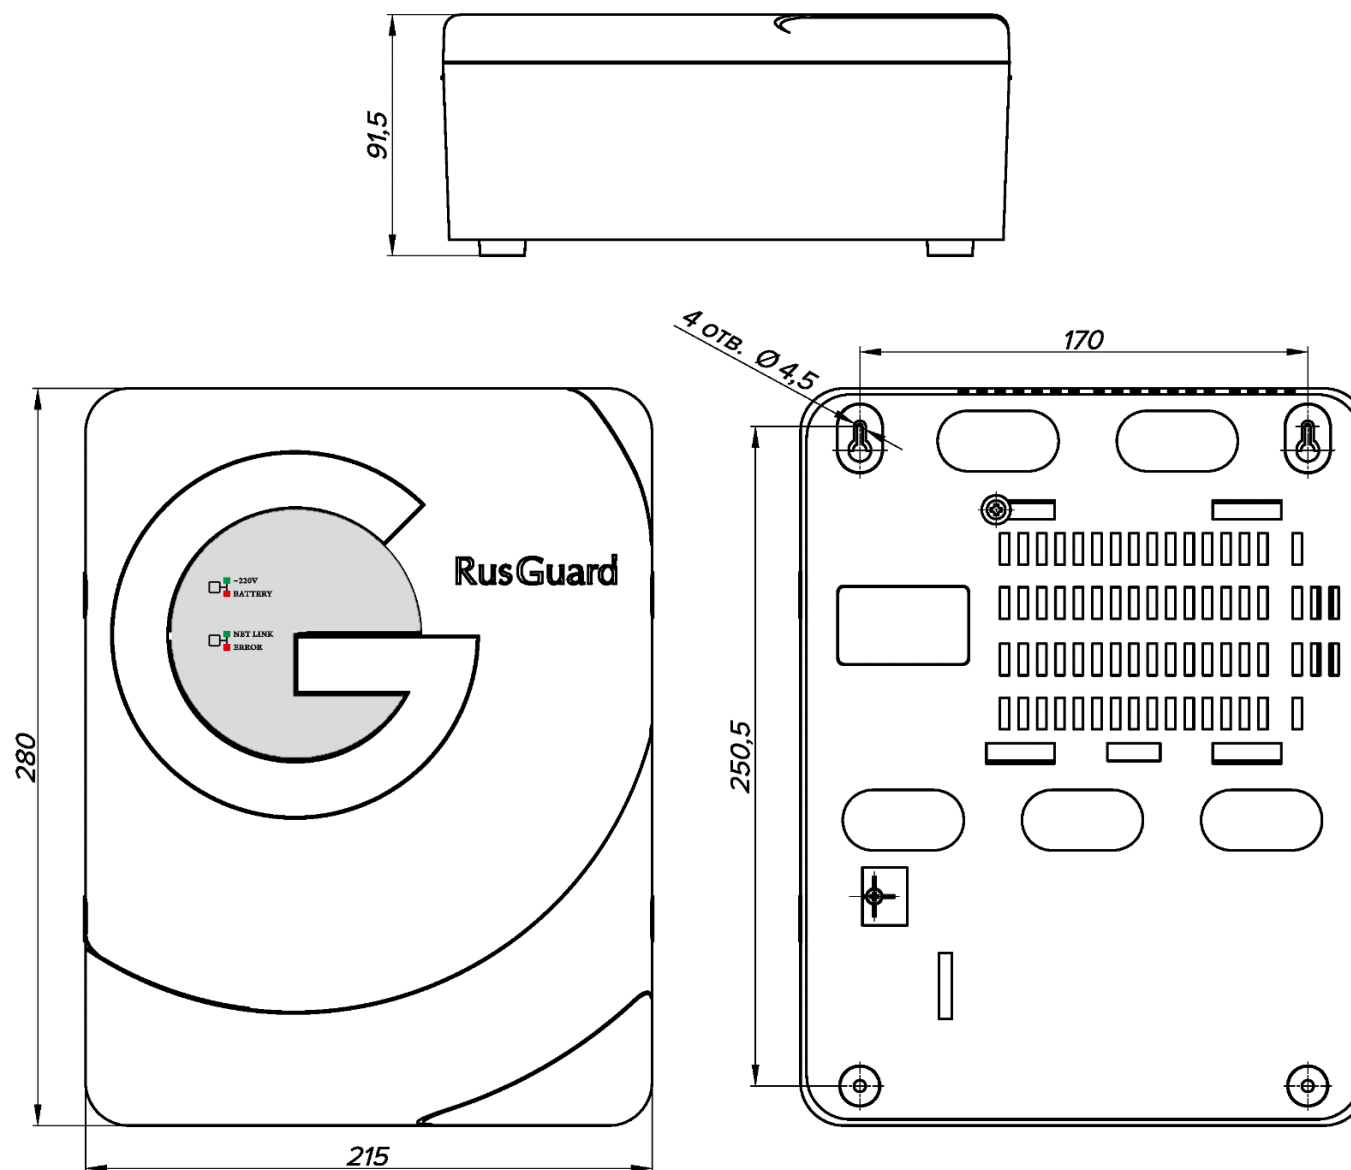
Габаритные размеры и крепеж контроллера в корпусе исполнения -В
